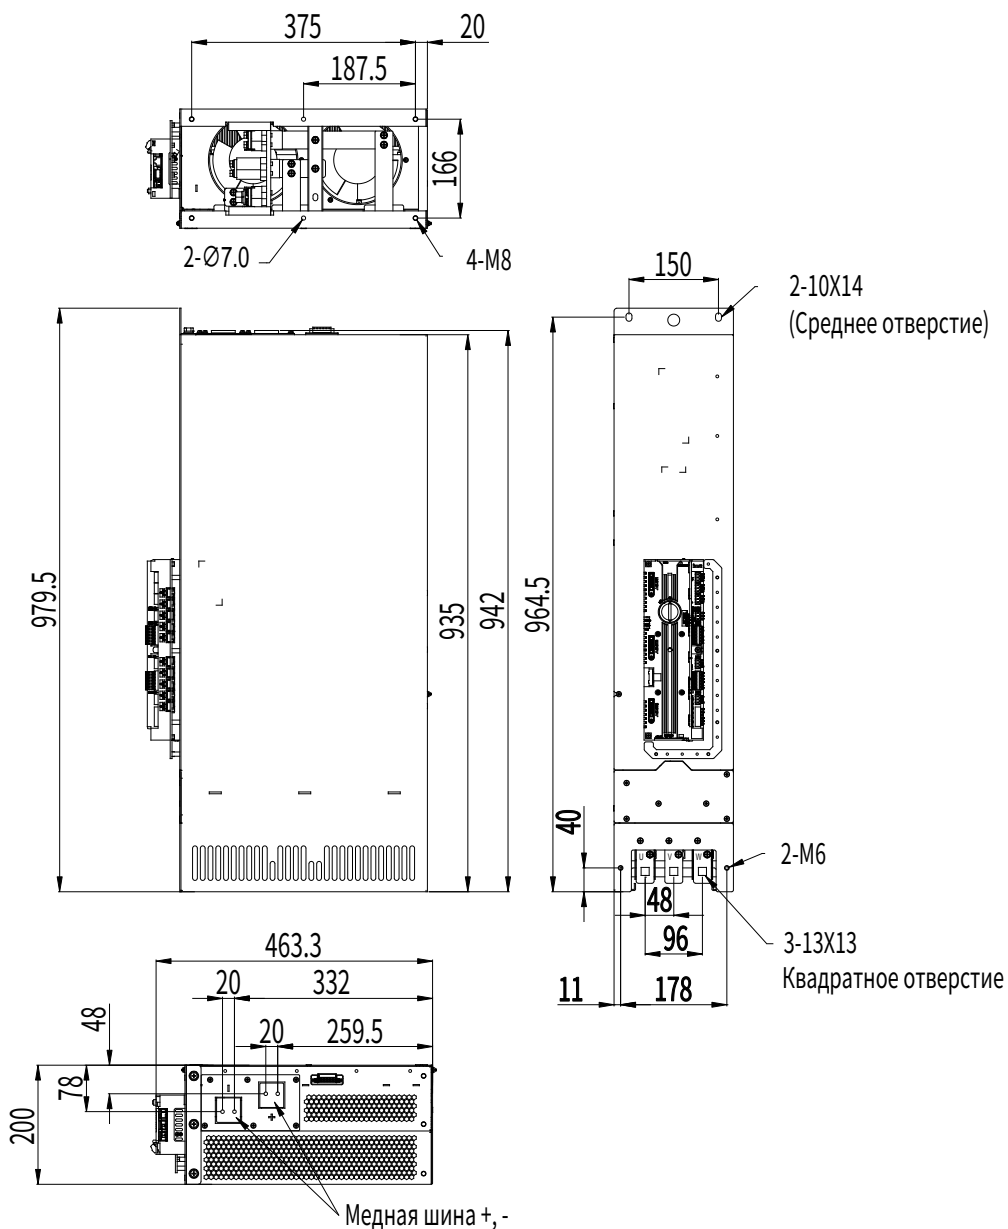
Установочные размеры инверторного блока А8i (единица измерения: мм)
